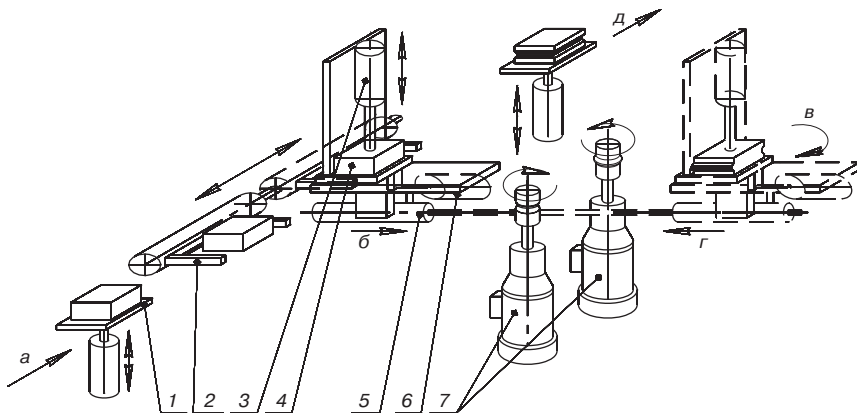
Схема установки фрезерования ШЛ 435: а – загрузка заготовок; б – прямая рабочая подача; в – поворот стола на 90°; г – обратная рабочая подача; д – сьем обработанных изделий; 1 – подъемник; 2 – питатель; 3 – прижим; 4 – обрабатываемая заготовка; 5 – механизм перемещения стола; 6 – механизм поворота стола; 7 – блок фрезерный
